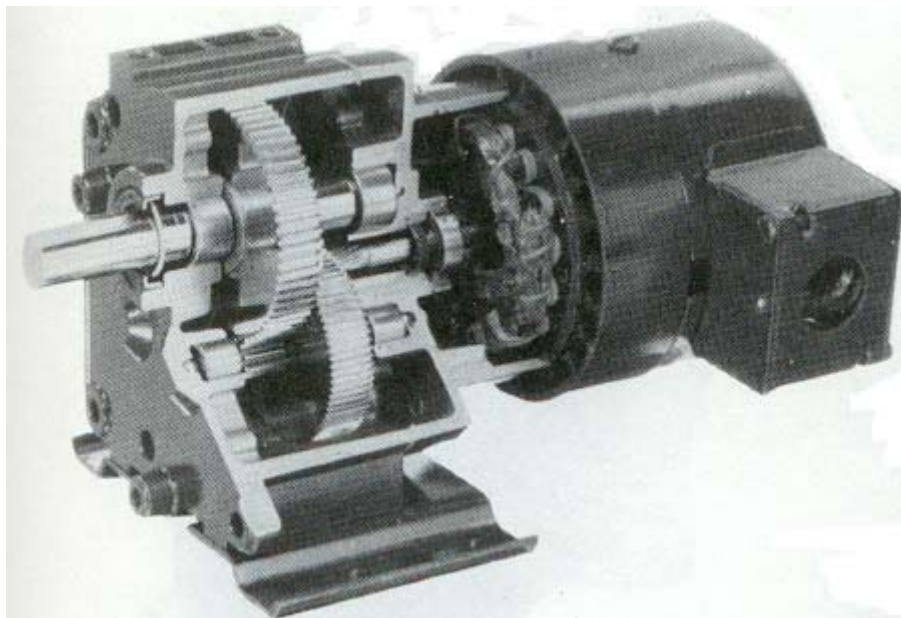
Reductor cilíndrico de dos etapas de engranajes de dientes rectos.
